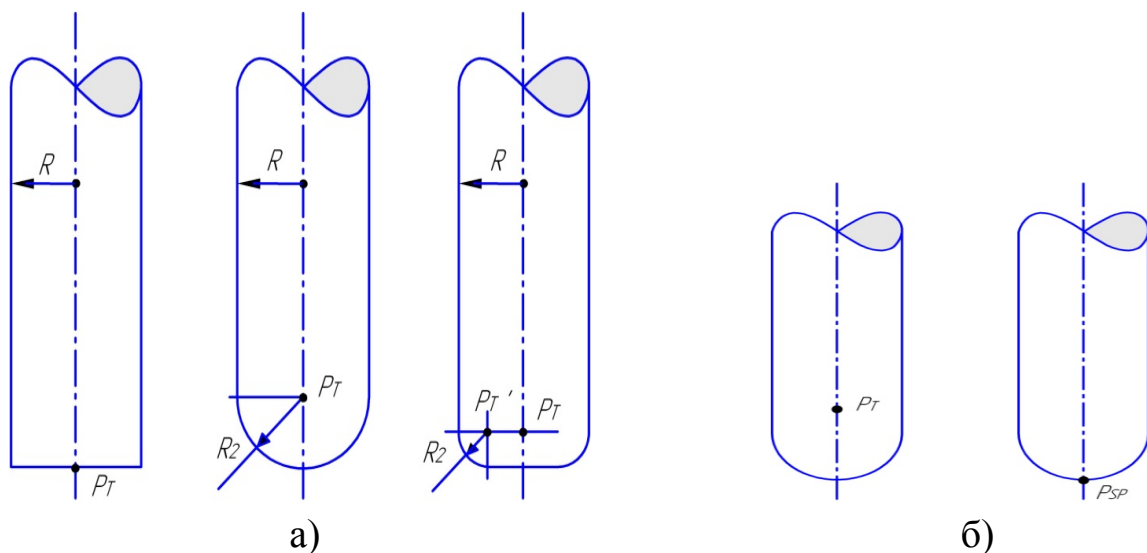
Направления нормали к обрабатываемой поверхности заготовки: а – в точках P_T ; б - в центре шара P_T и полюса шара P_{SP} .
